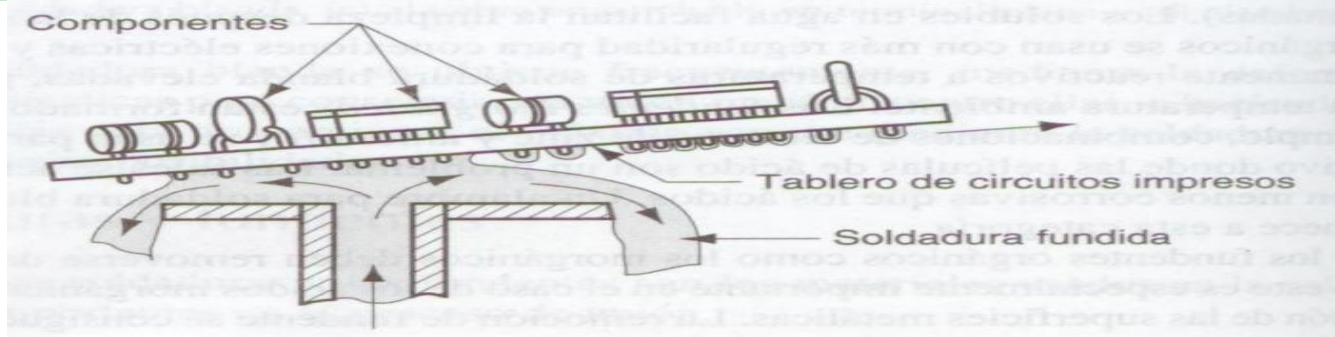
Soldadura blanda en olas, en la cual se aplica soldante fundido a través de un orificio estrecho sobre la parte inferior de un tablero de circuitos impresos para conectar los alambres de plomo componentes.
